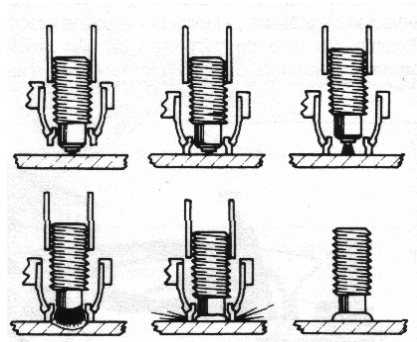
Procedimiento de soldadura de un perno.
